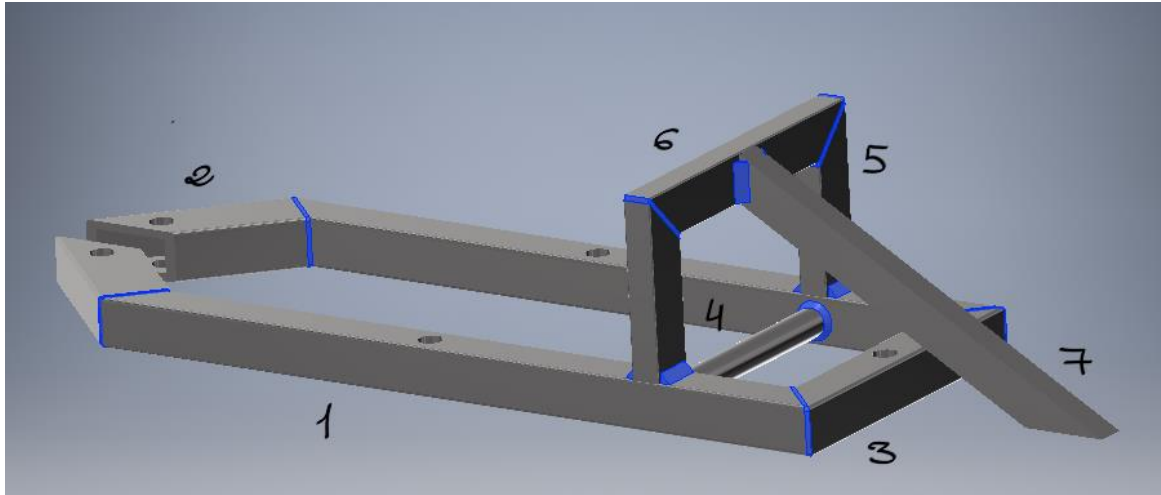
Estructura soporte en la que los cordones de soldadura están coloreados en azul.
